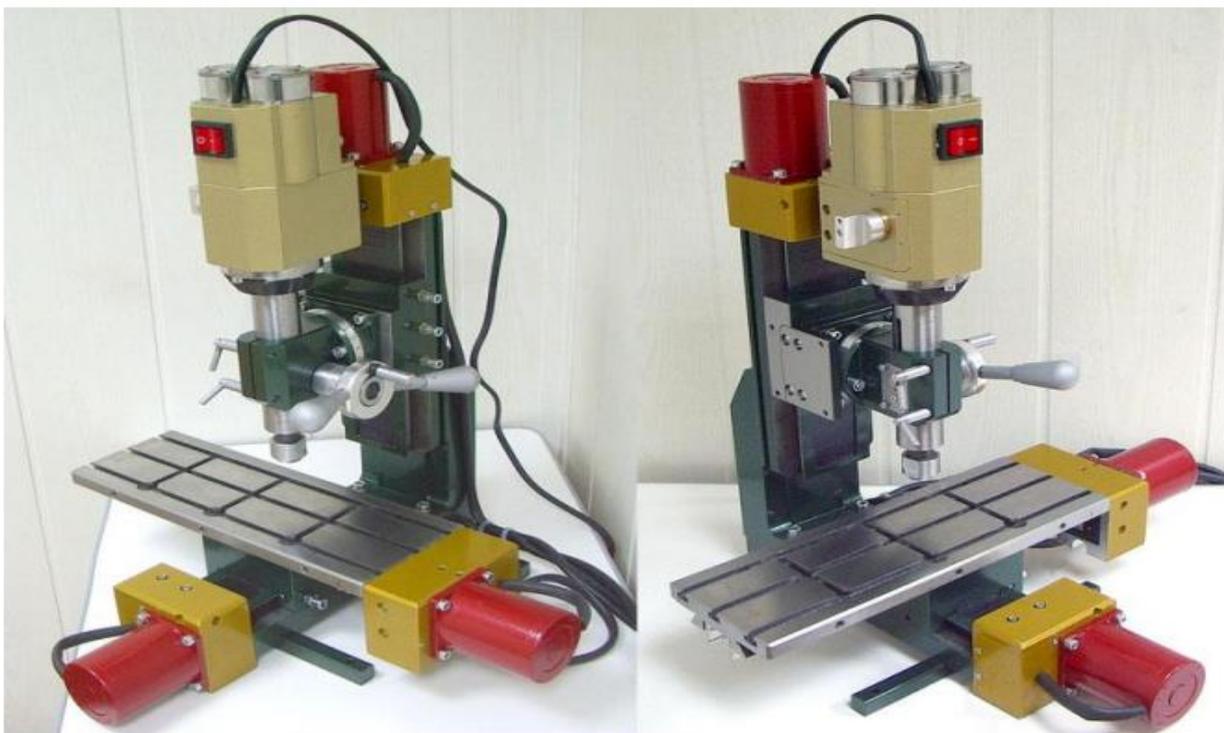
Малогабаритный широкоуниверсальный станок МШ-2.2.
